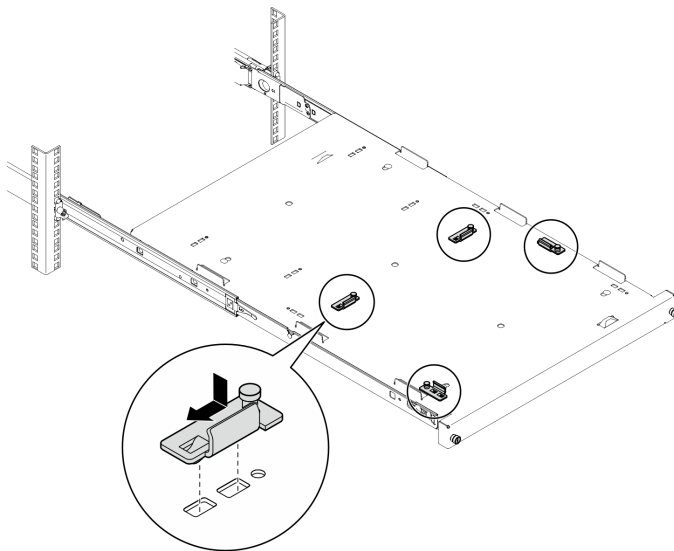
Installieren der Halterungen am Einbaurahmen
